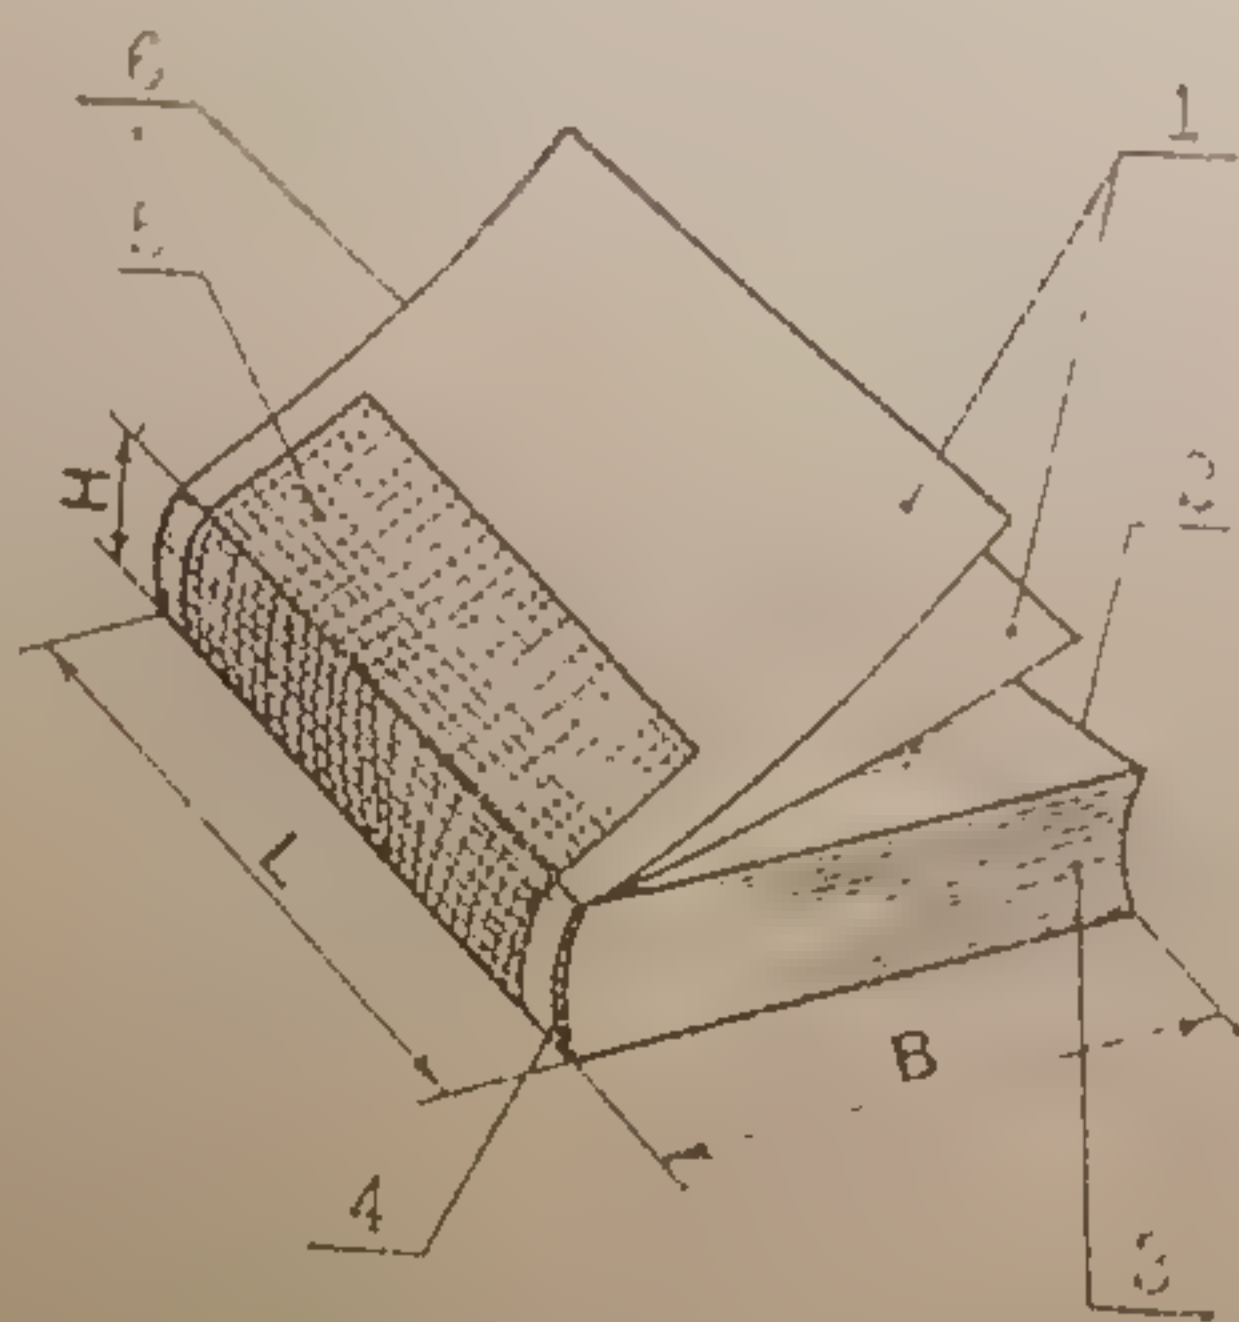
Книжный блок: 1 — форзац; 2 — передний обрез блока; 3 — нижний обрез блока; 4 — каптал; 5 — марля; 6 — верхний обрез блока; B — ширина блока; L — длина блока; H — толщина блока
